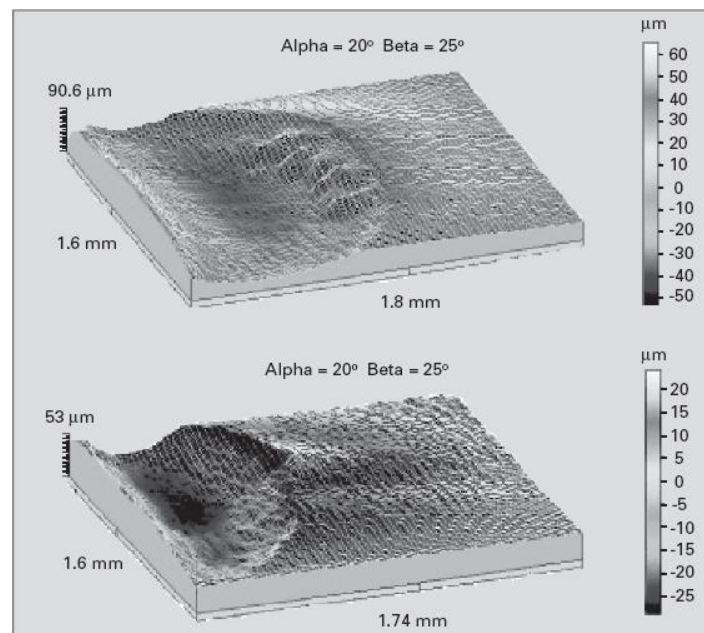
Perfis de superfícies de saída de ferramentas de metal duro após usinagem de aço endurecido por 16 min: a) sem revestimento; b) revestida com TiAlN
